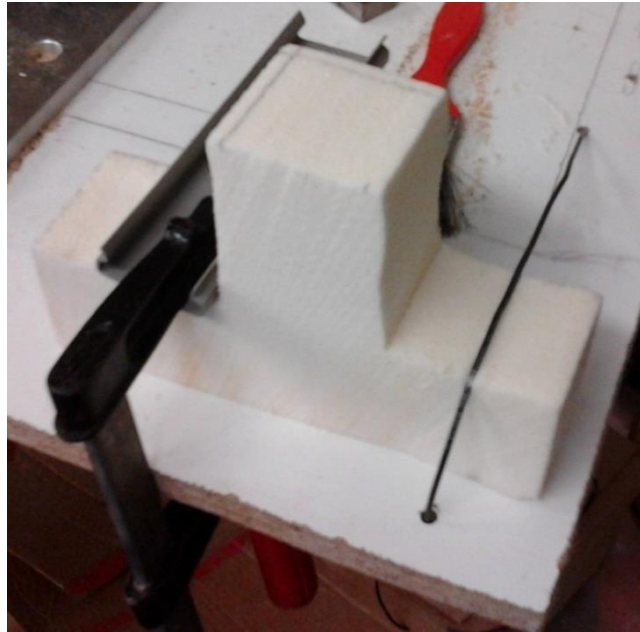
Bloco de material para o primeiro ensaio de maquinagem do puzzle.
